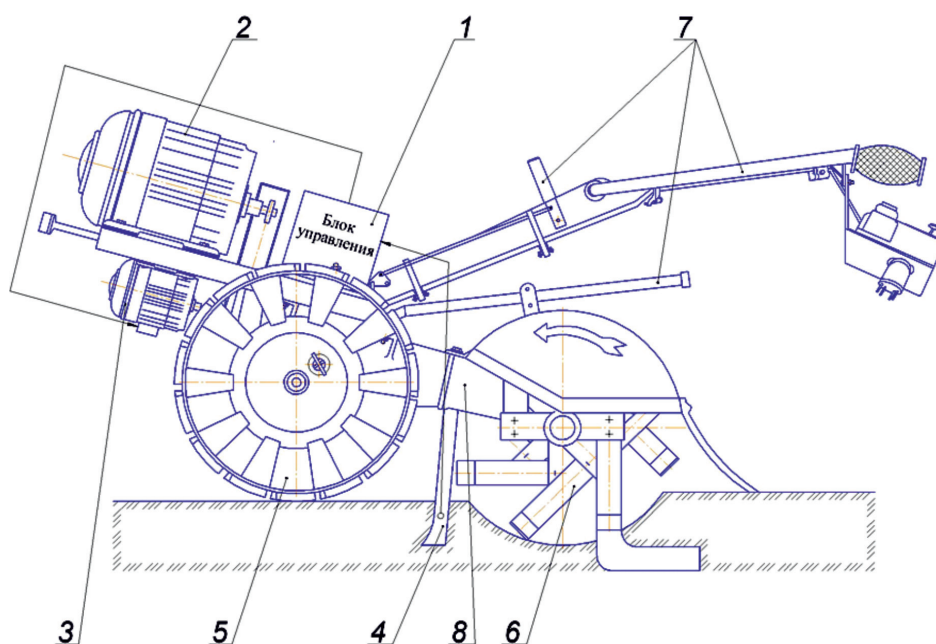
Схема адаптивной фрезы: 1 – блок управления с обратной связью; 2 – электродвигатель привода рабочих органов; 3 – электродвигатель привода ходовых колес; 4 – сканер твердости почвы; 5 – ходовые колеса; 6 – рабочие органы; 7 – органы управления; 8 – редуктор
